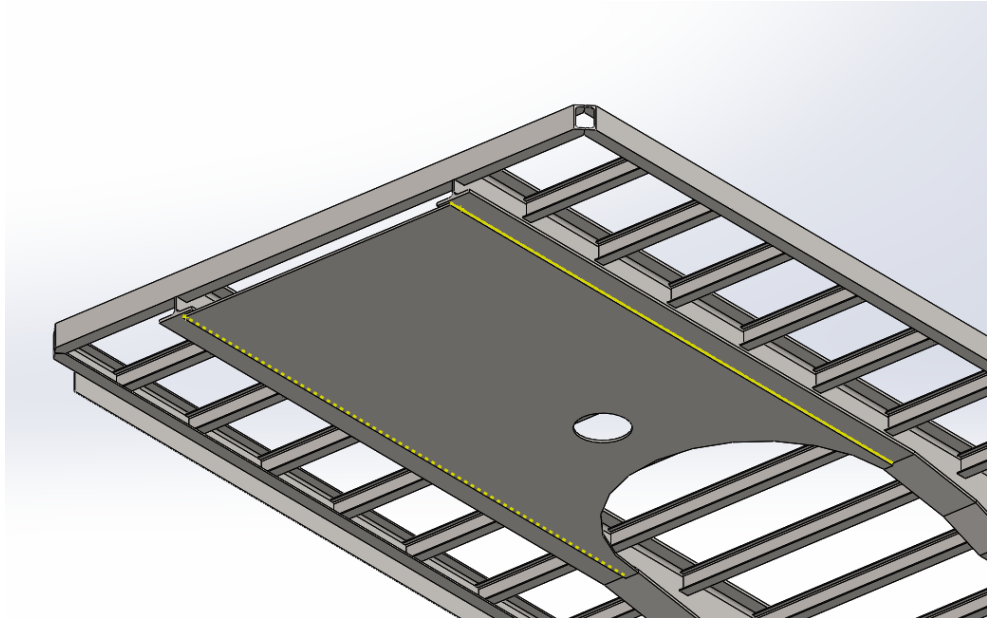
Detalle de unión de placa de apoyo King Pin
